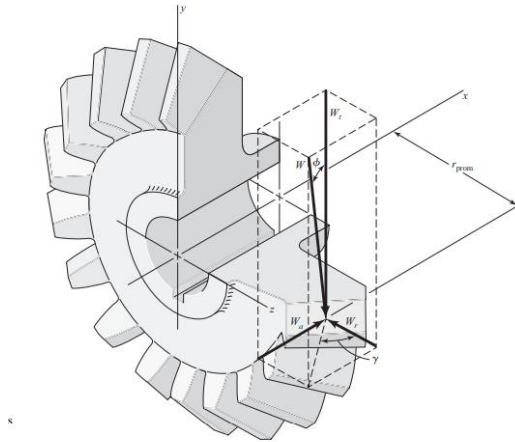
Componentes de la fuerza resultante en u engranaje cónico[41]
